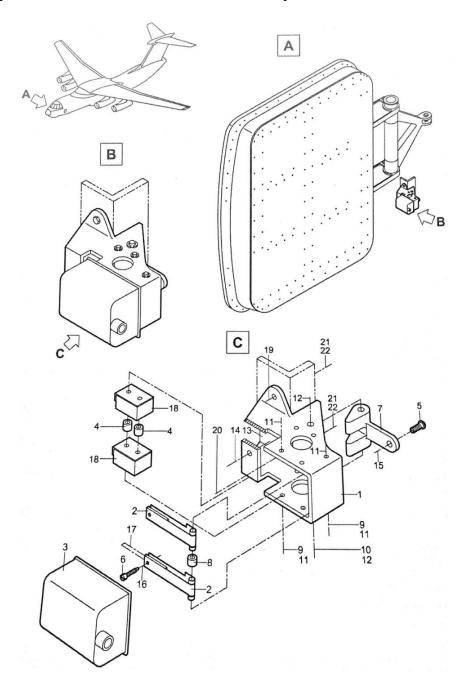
Пример эскиза сборочной единицы каталога деталей
